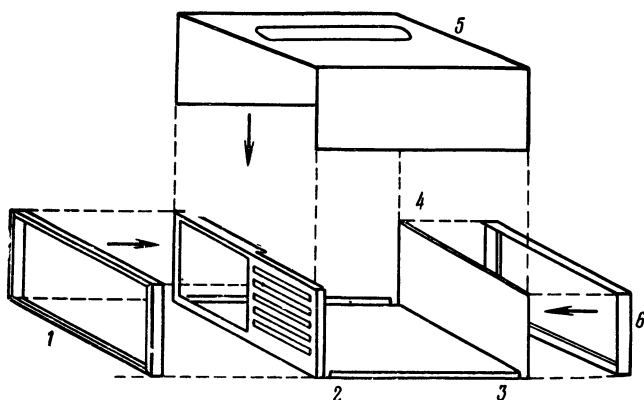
Эскиз составных деталей корпуса телевизора «Микрон».
